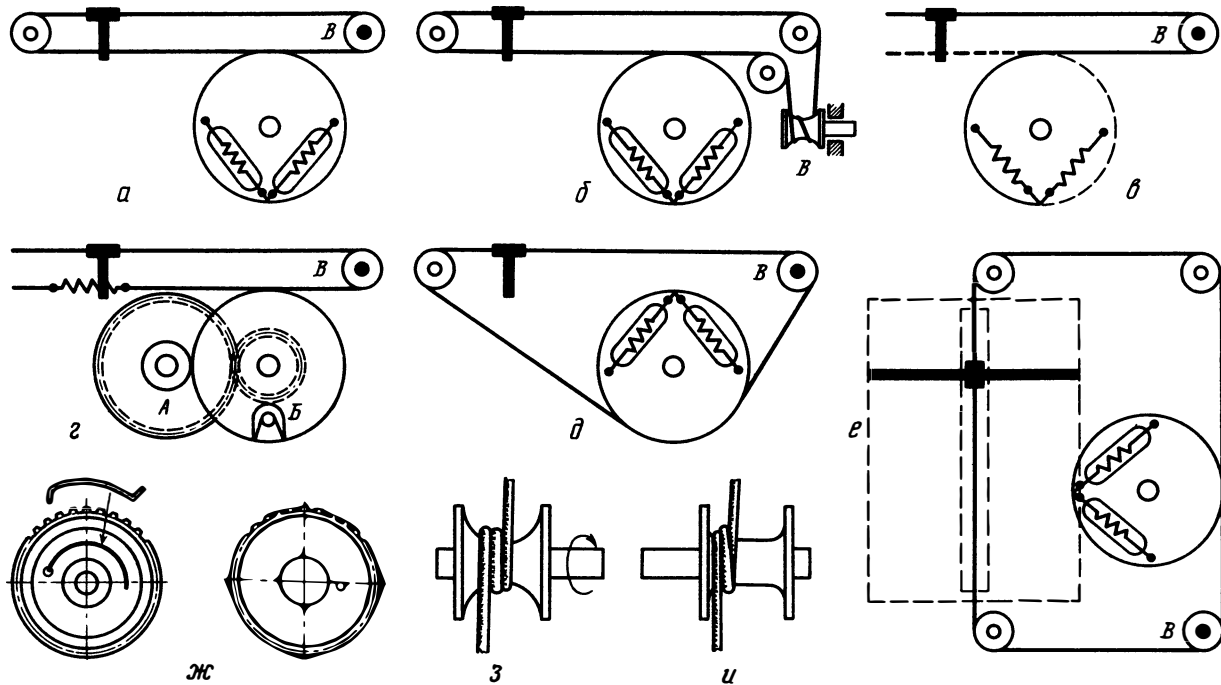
Примеры кинематических схем и конструктивных элементов верньеров:
